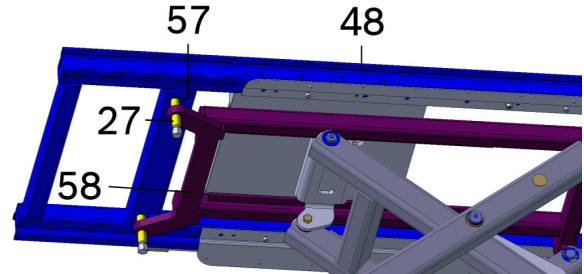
Piano elevatore a pantografo senza piattaforme dal basso
